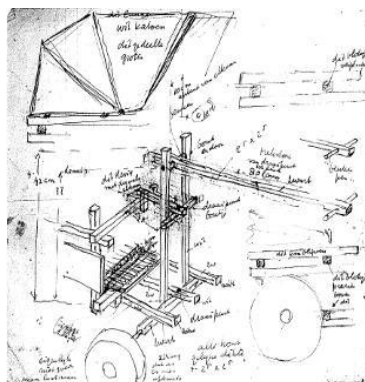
Dibujos constructivos con proyección isométrica y detalles en alzado.
